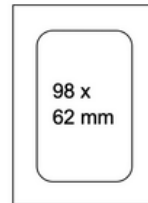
Geometrische Aufnahme für Befestigungssystem (längs)
